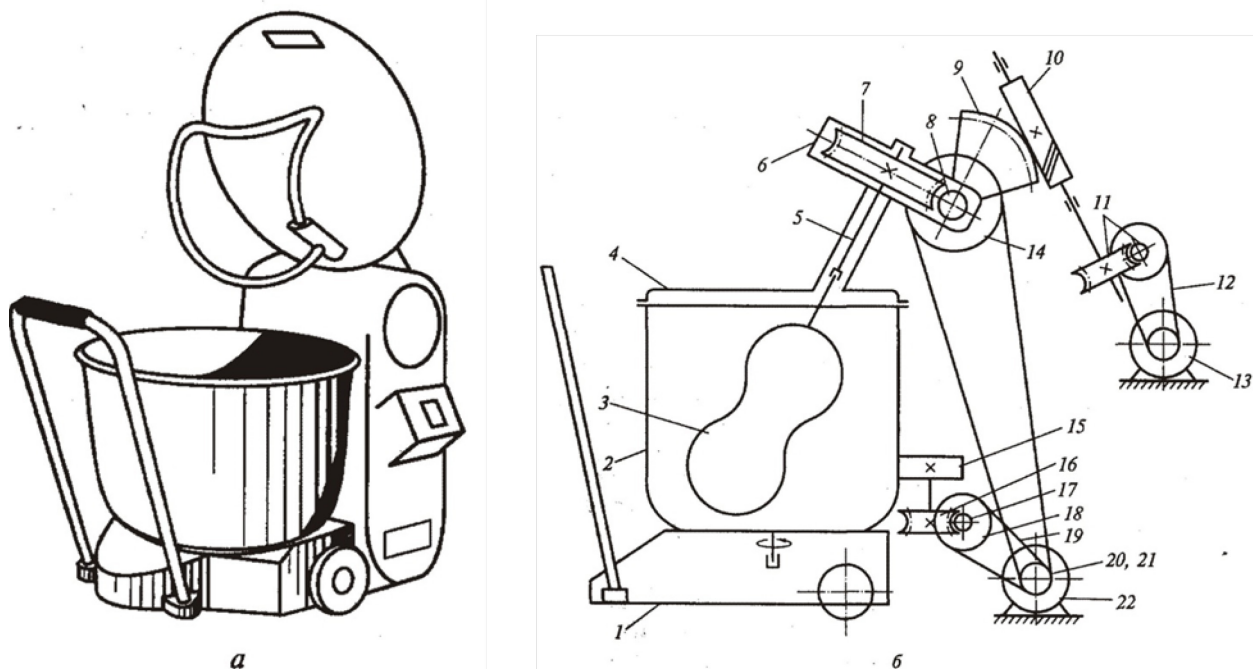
Тістомісильна машина МБТМ-140: а – загальний вид; б – кінематична схема: 1 – візок; 2 – діжа; 3 – робочий орган; 4 – кришка; 5 – робочий вал; 6 – корпус траверси; 7, 16 – черв'ячне колесо; 8, 10, 17 – черв'як; 9 – черв'ячний сектор; 11 – черв'ячна передача; 12 – клинопасова передача; 13 – реверсивний електродвигун; 14, 18, 20, 21 – шківни; 15 – фрикційне колесо; 19 – клиновидний пас; 22 – електродвигун
